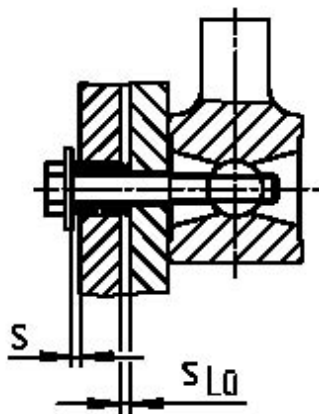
Änderung des Bremsmomentes / Adjusting the braking torque / Modification du couple de freinage
